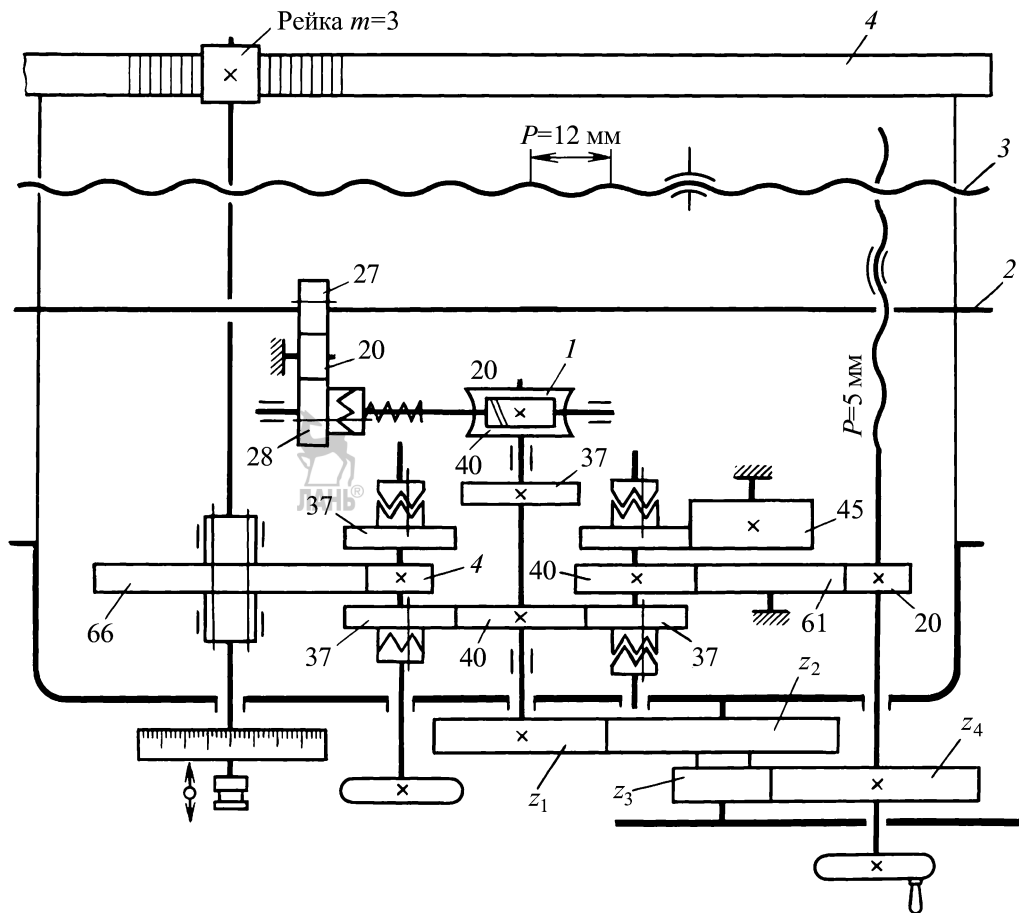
Гитара станка 1К62 для передачи вращения на винт поперечного суппорта:
